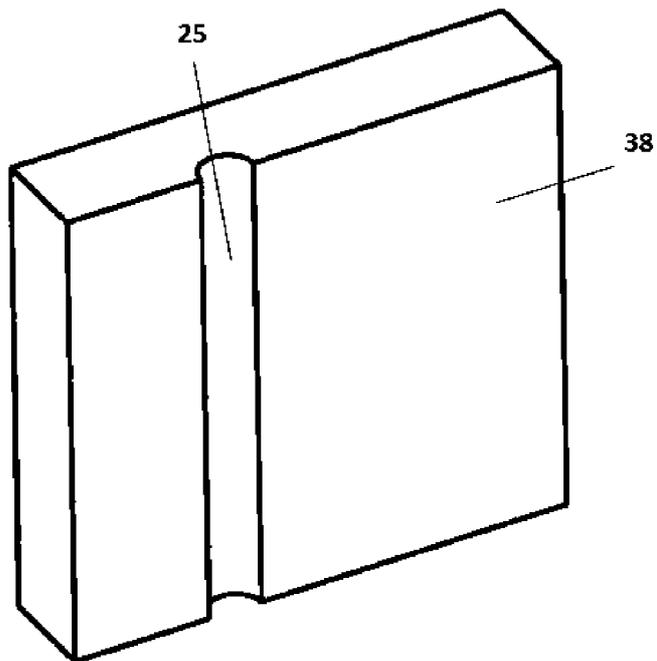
Увеличенный вид модуля печатающей головки: область подачи краски
